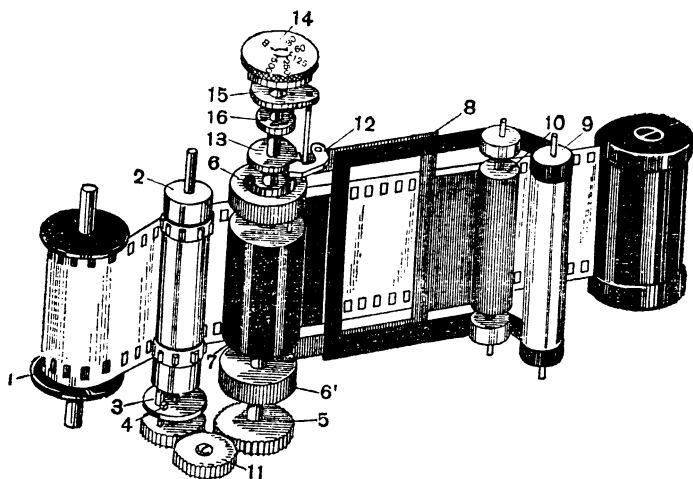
Принципиальная схема шторного затвора: 1 — приемная катушка; 2 — ось мерного валика; 3 — палец мерного валика; 4 — зуб; 5 — зубчатое колесо; 6 и 6' — шкивы; 7 — барабан; 8 — шторки; 9 и 10 — гильзы; 11 — зубчатое колесо-ограничитель; 12 — тормозная защелка; 13 — диск с короткой и длинной шпильками; 14 — головка установки выдержек; 15 — диск с двумя шпильками; 16 — диск с отверстием для короткой шпильки
